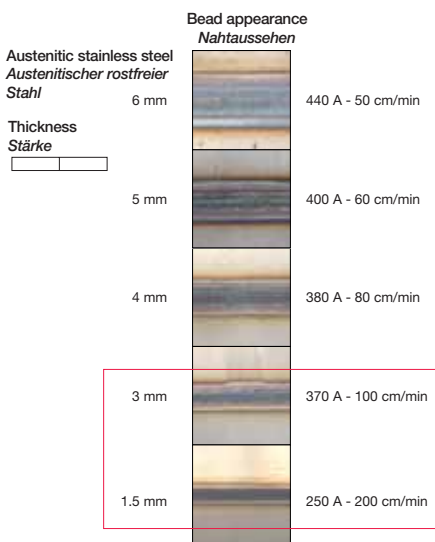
Test mit gleichem Brenner, Schutzgasdüse dem Schweißstrom angepasst
